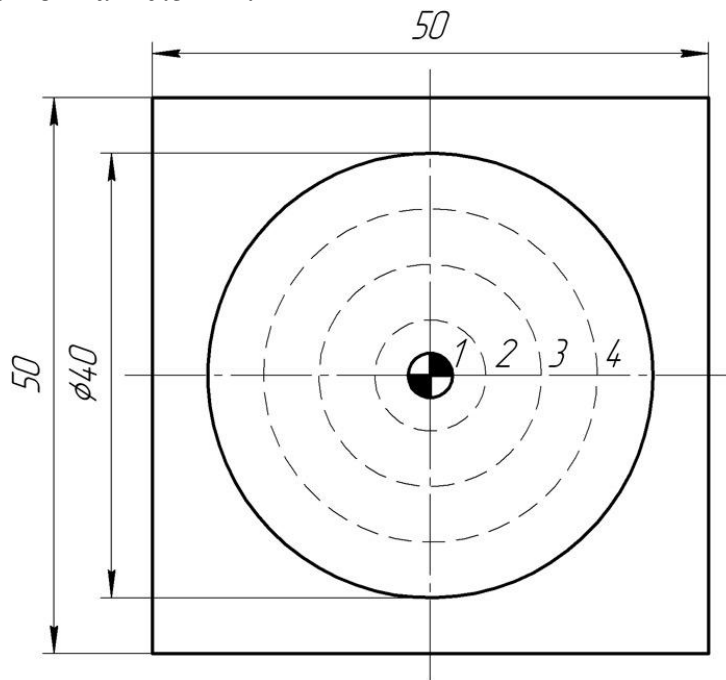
Чорнове фрезерування круглої кишені
